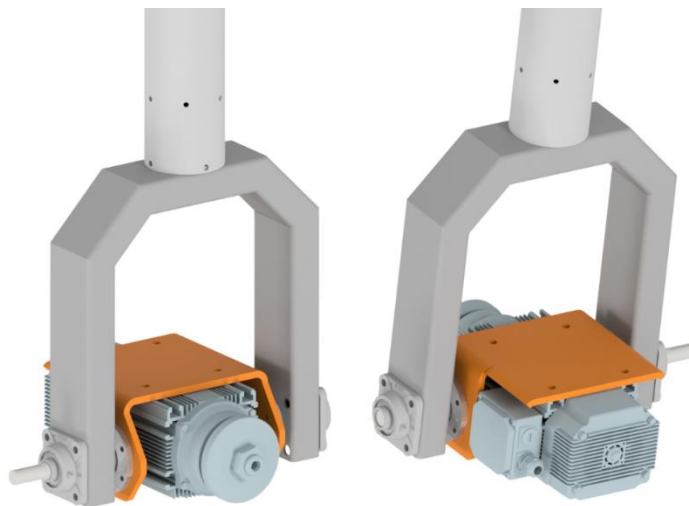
Conjunto del motor principal montado en la “horquilla”.
